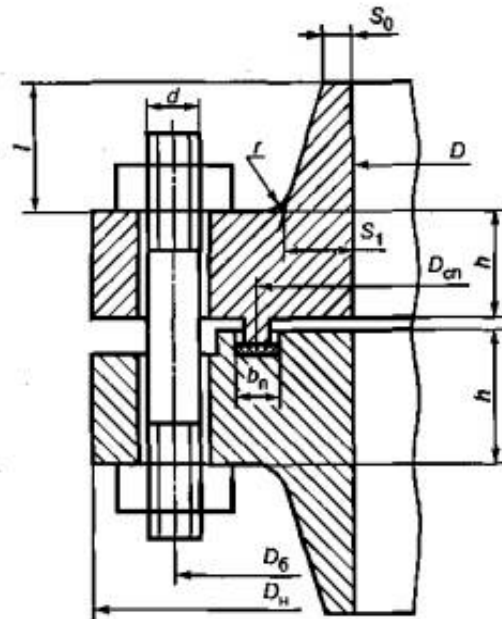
Фланцевое соединения с приварными встык фланцами с гладкой уплотнительной поверхностью типа шип - паз.
